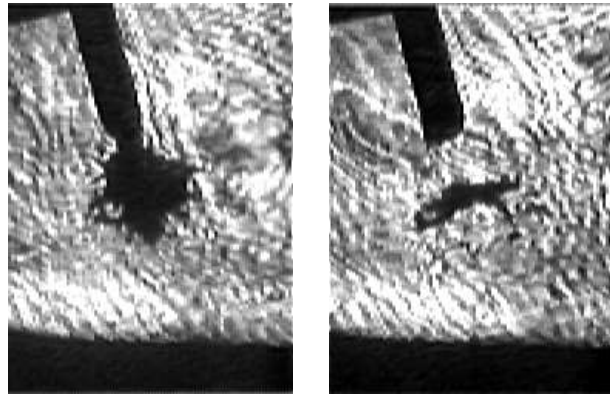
Transferência explosiva na soldagem GMAW com eletrodo Al-Mg 1,2 mm. (Cortesia: Prof. Américo Scotti, Universidade Federal de Uberlândia).
